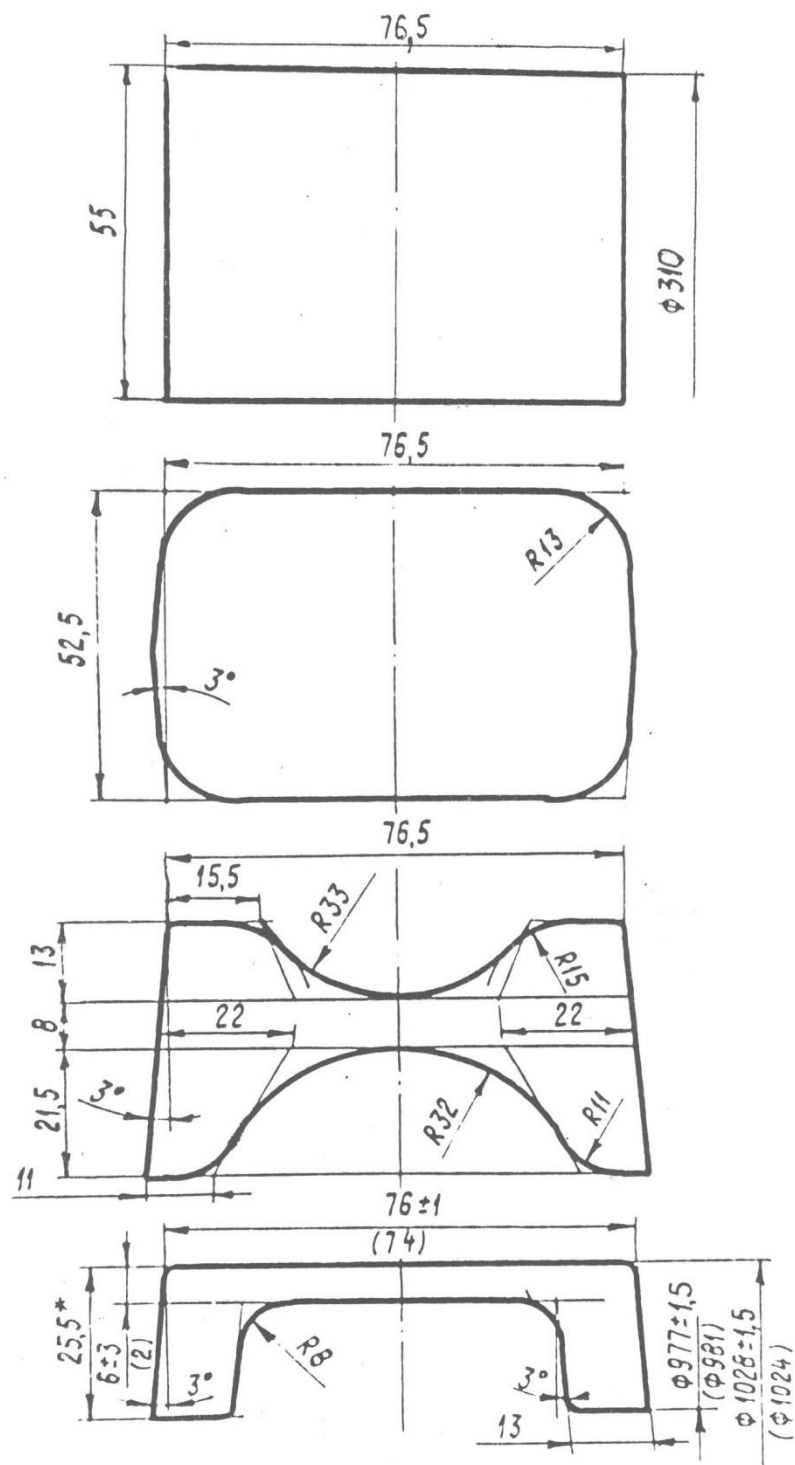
Калибровка заготовок промежуточного кольца компрессора из сплава ВТ20
